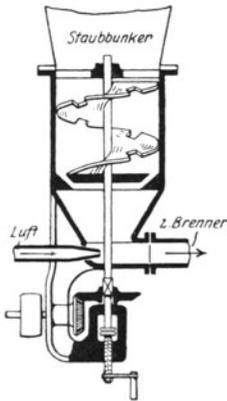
Fuller S-H-Speiser mit Rührwerk¹⁾.
